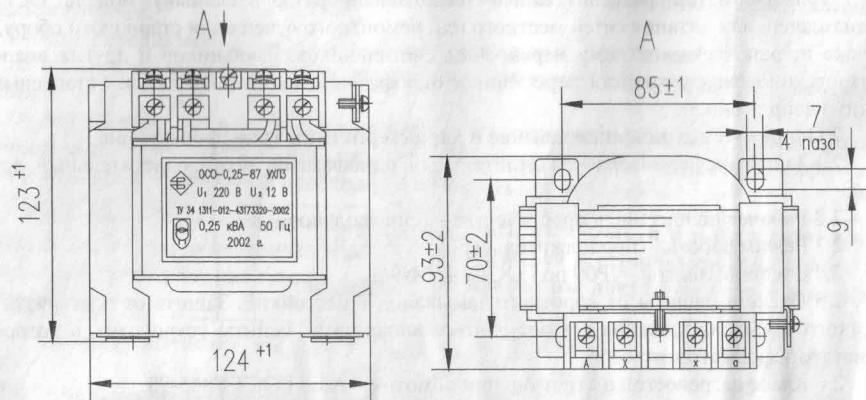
Общий вид трансформатора, его габаритные и установочные размеры.
